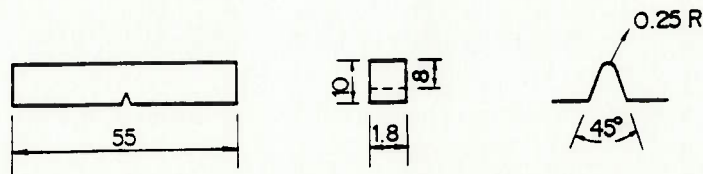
Dimensões dos corpos de prova para o ensaio de impacto Charpy com entalhe em V
